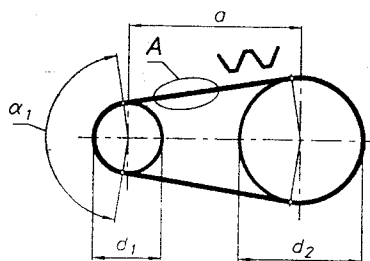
Схема и основные размеры зубчато-ременной передачи
